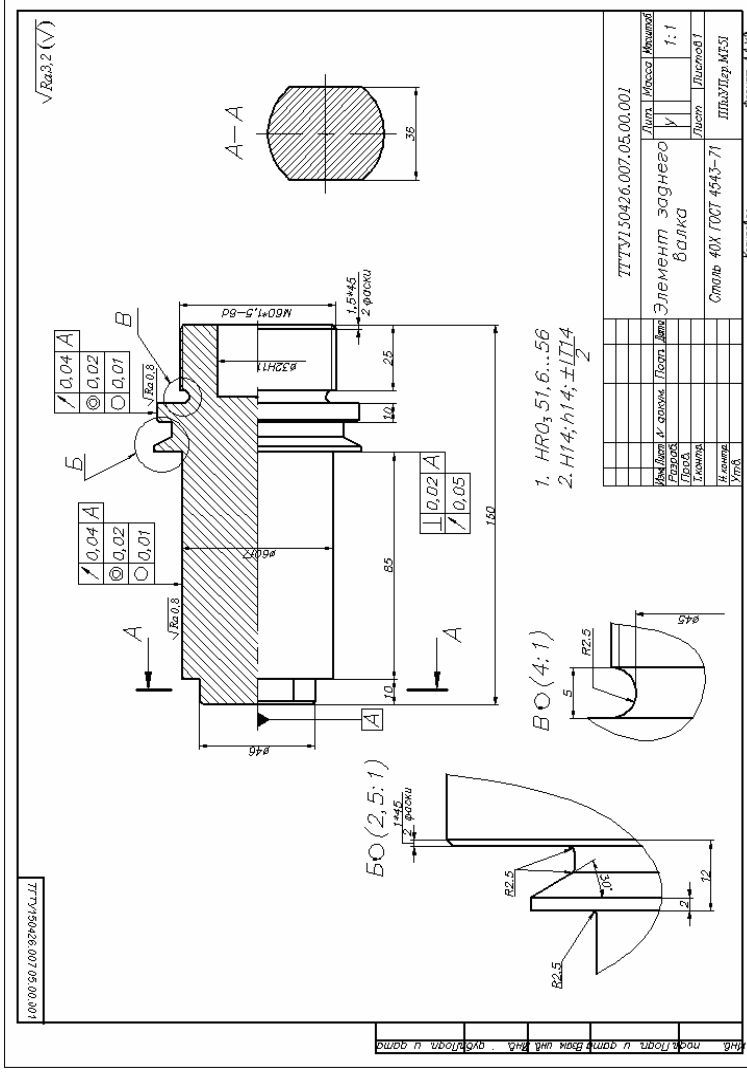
Рабочий чертеж левого элемента заднего валика вальцев
